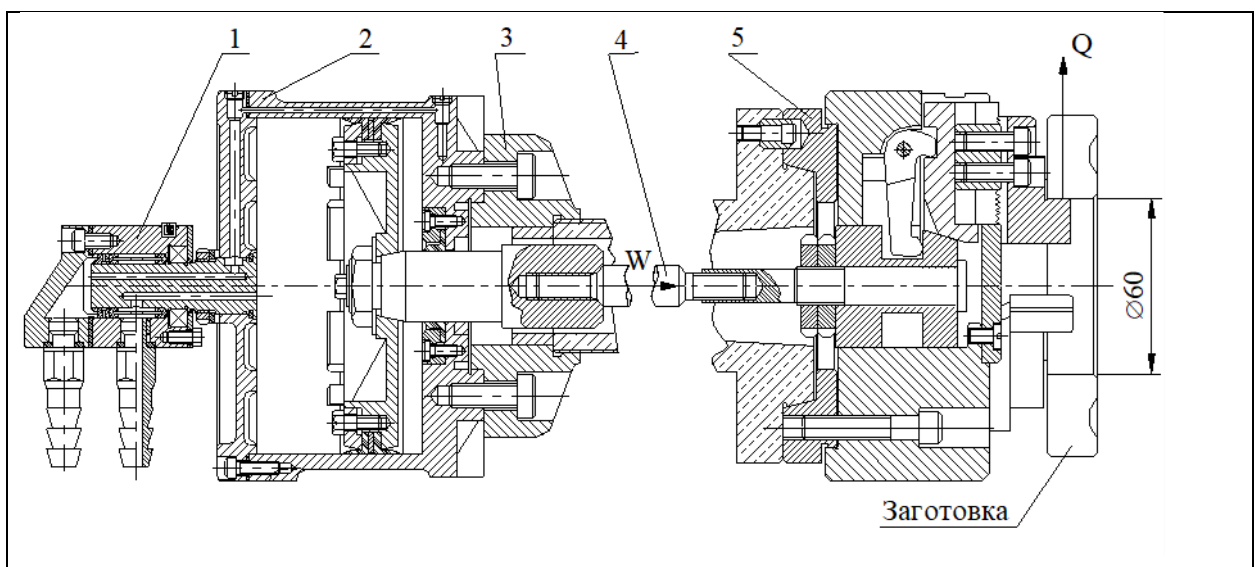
Загальна компоновка патрона з пневматичним приводом, що обертається, на токарному верстаті: 1-муфта для підведення стисненого
